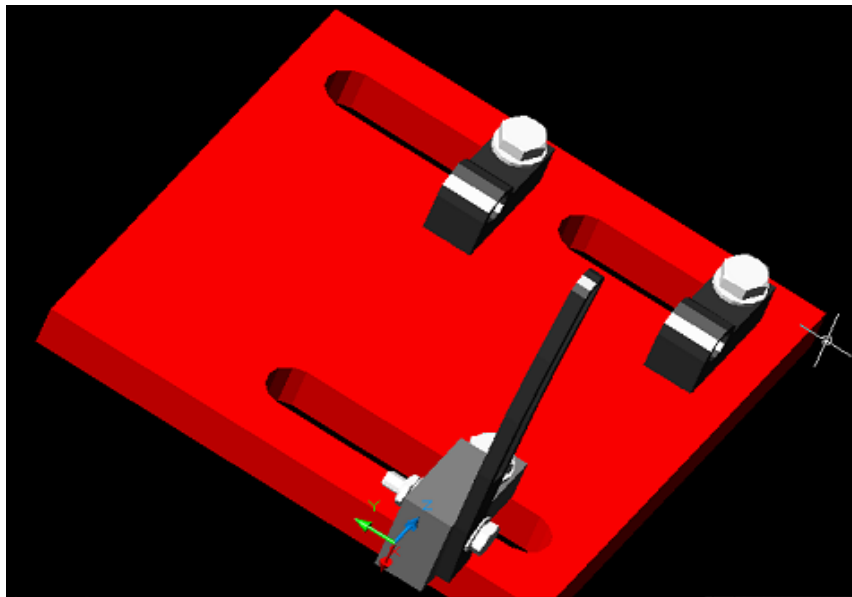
Vista isométrica 3 de la placa que soporta el alternador
